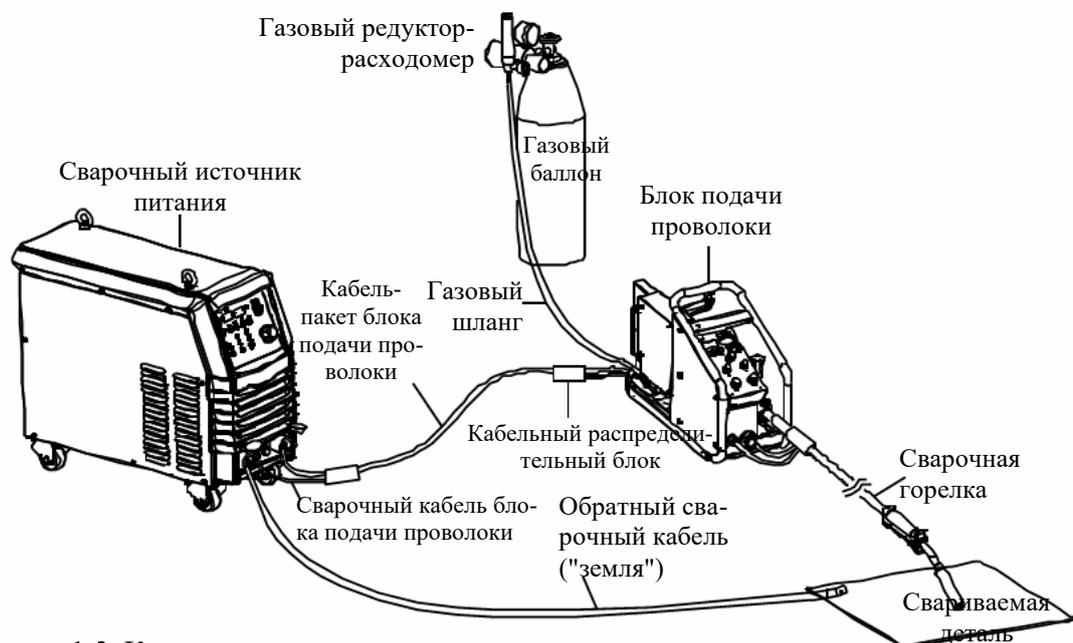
Компоненты сварочного аппарата
